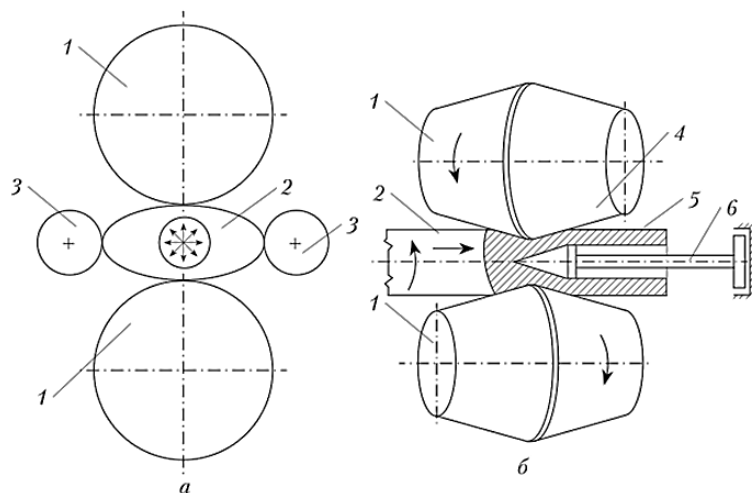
Поперечно-винтовая прокатка заготовки трубы (гильзы):
